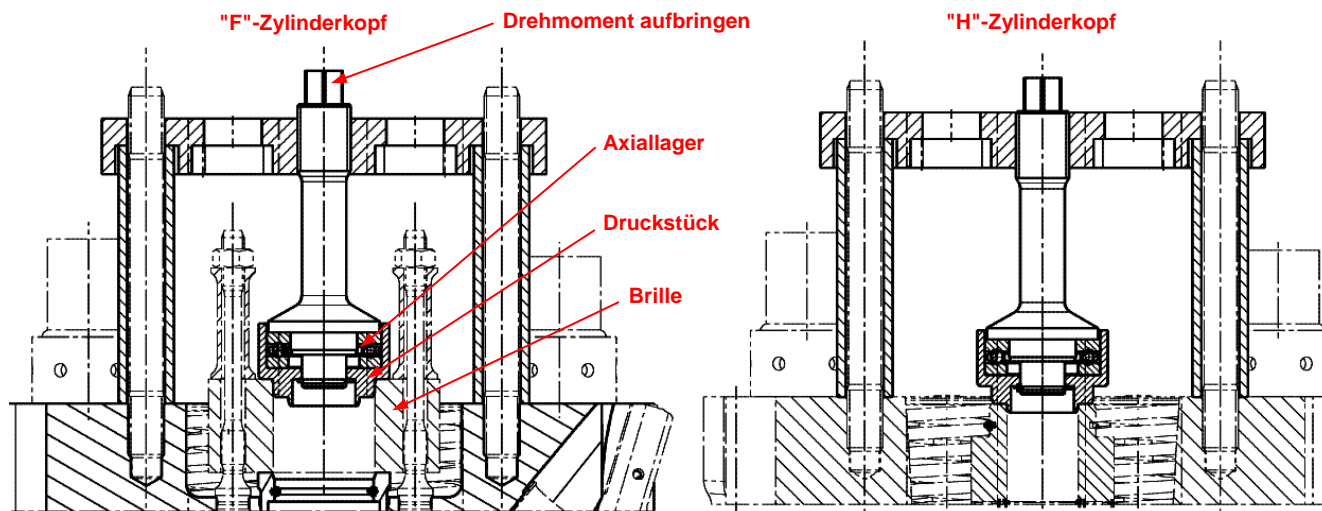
Positionierung des Druckstücks auf der Brille, "F"- und "H"-Zylinderkopf
